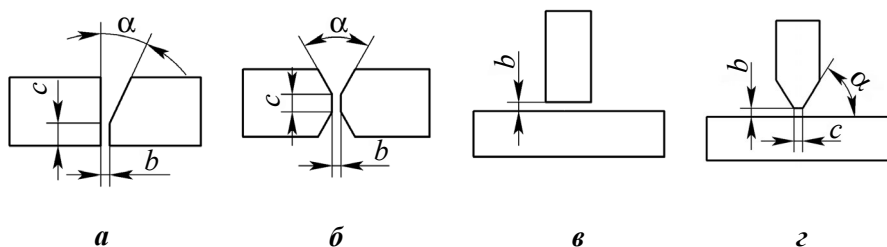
Приклади підготовки крайок зварних з'єднань:
